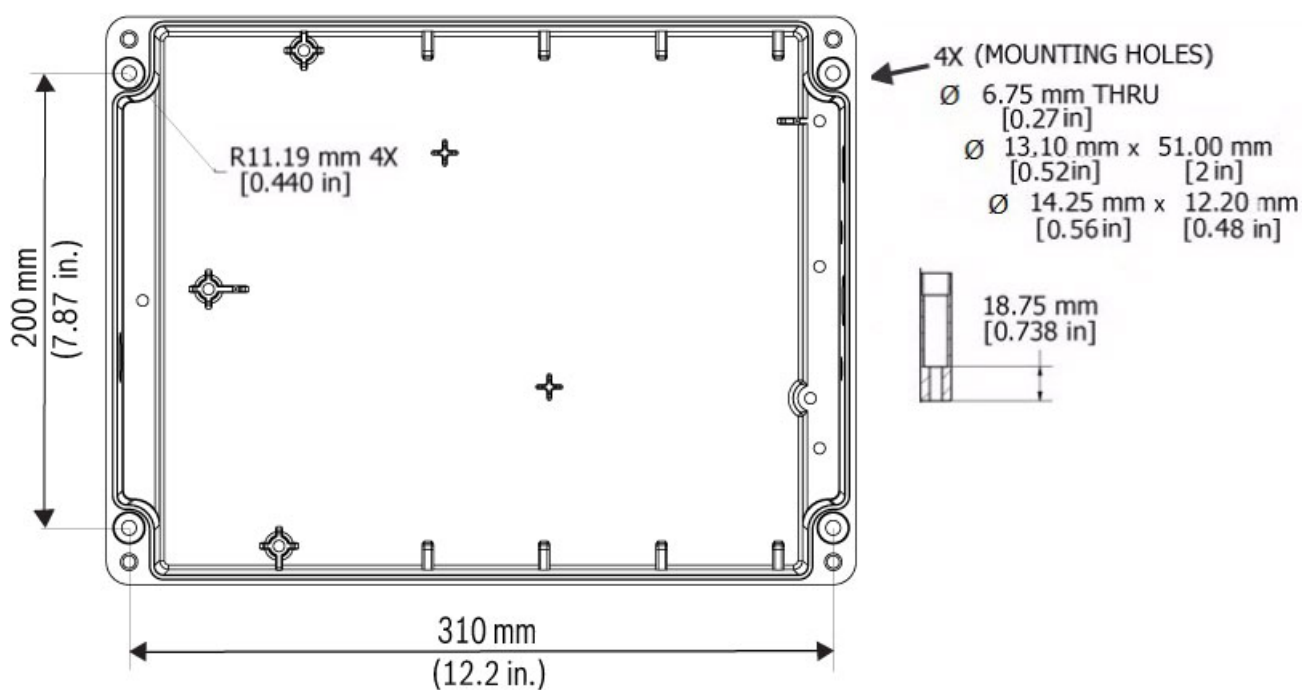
Dimensões, orifícios de montagem, VIDEOJET connect 7000
